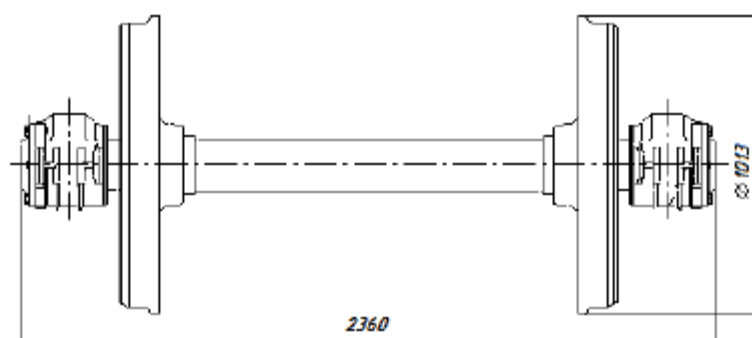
Колесные пары типа РУ1Ш-957-Г, РВ2Ш-957-Г или РУ1-957-Г с подшипниками в корпусе буксы. Габаритные размеры
